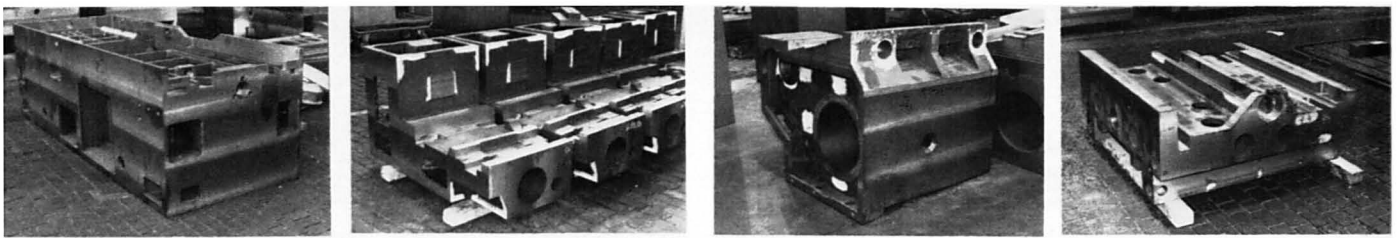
Beispiele typischer Werkstücke für die 5-Seiten-Bearbeitung auf vertikalen Bearbeitungszentren
